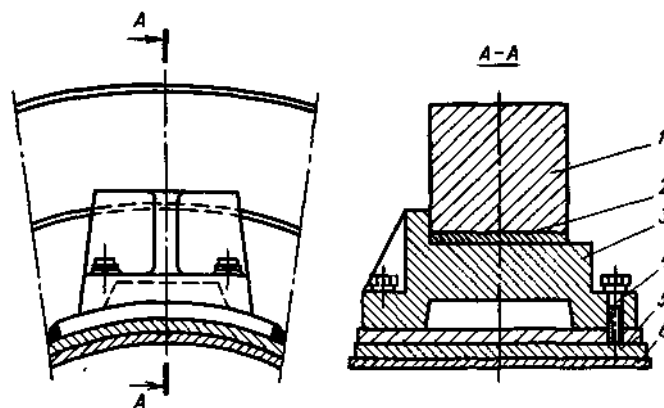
Вузол кріплення бандажа до барабана
